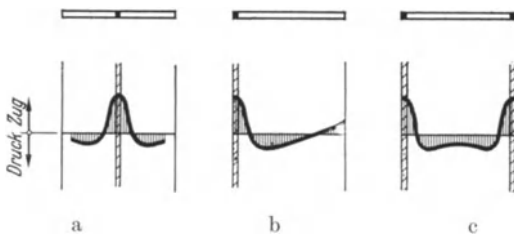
Längsschweißspannungen infolge von Längsnähten.
